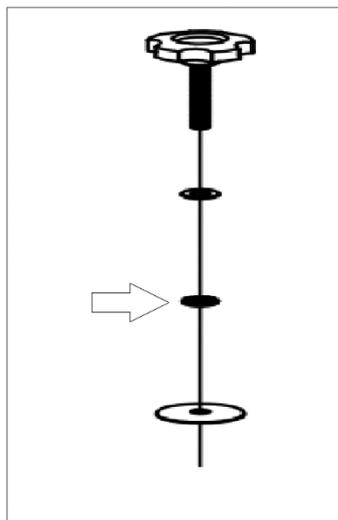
Explosionszeichnung der kompletten Baugruppe.
